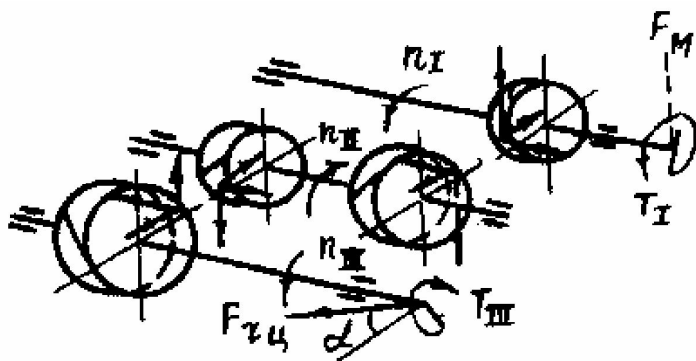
Пример силовой расчетной схемы валов передаточного механизма (редуктора) ленточного конвейера, кинематическая схема которого показана на рис. 3.1
